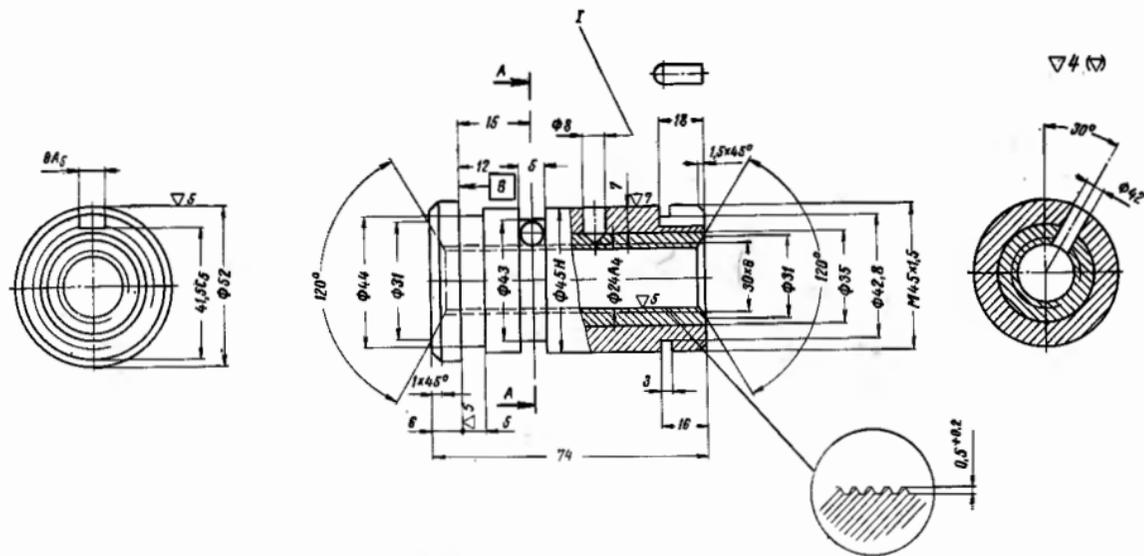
Гайка биметаллическая. Деталь 6М82-7-103
